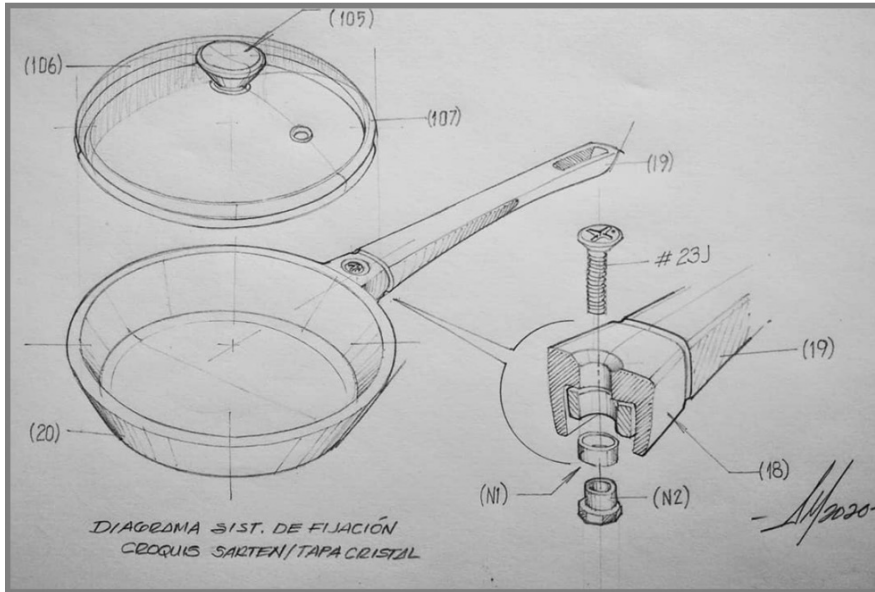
Bocetaje detalle vista corte transversal solución de ensamble asidera/sartén.
